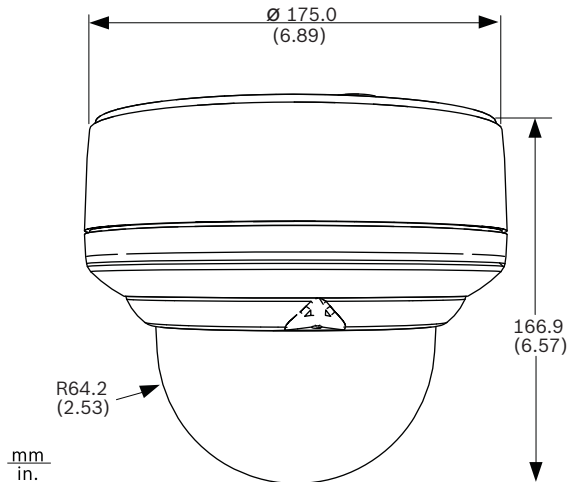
Dimensões do suporte para montagem saliente para interior
